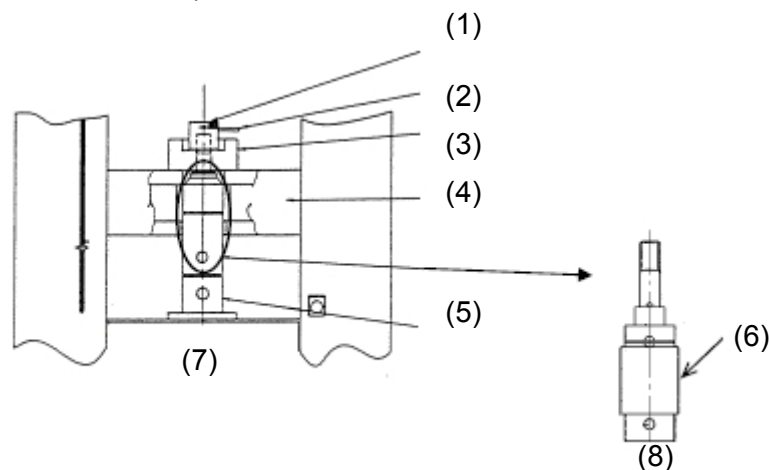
(b) Montaż łącznika uniwersalnego
